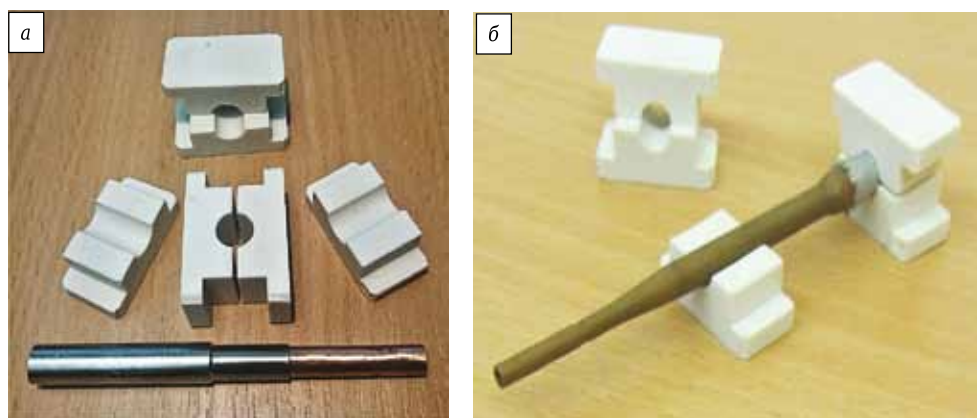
Электроизоляторы для установок автоматической контактной сварки трубчатых элементов медь – алюминий
